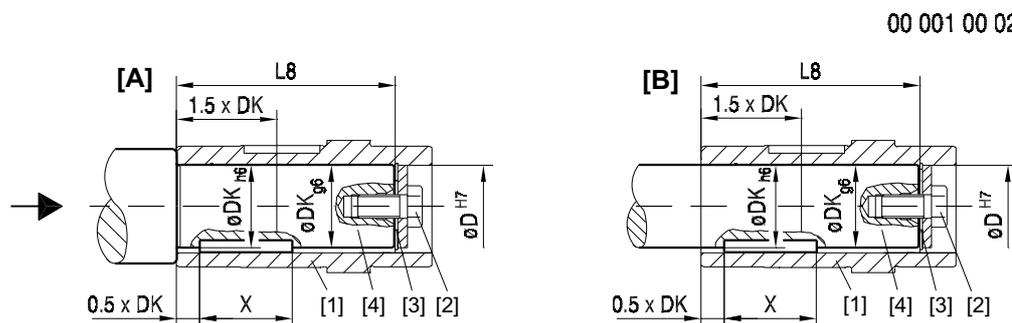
Ведомый вал с опорным выступом (A) и без опорного выступа (B)
